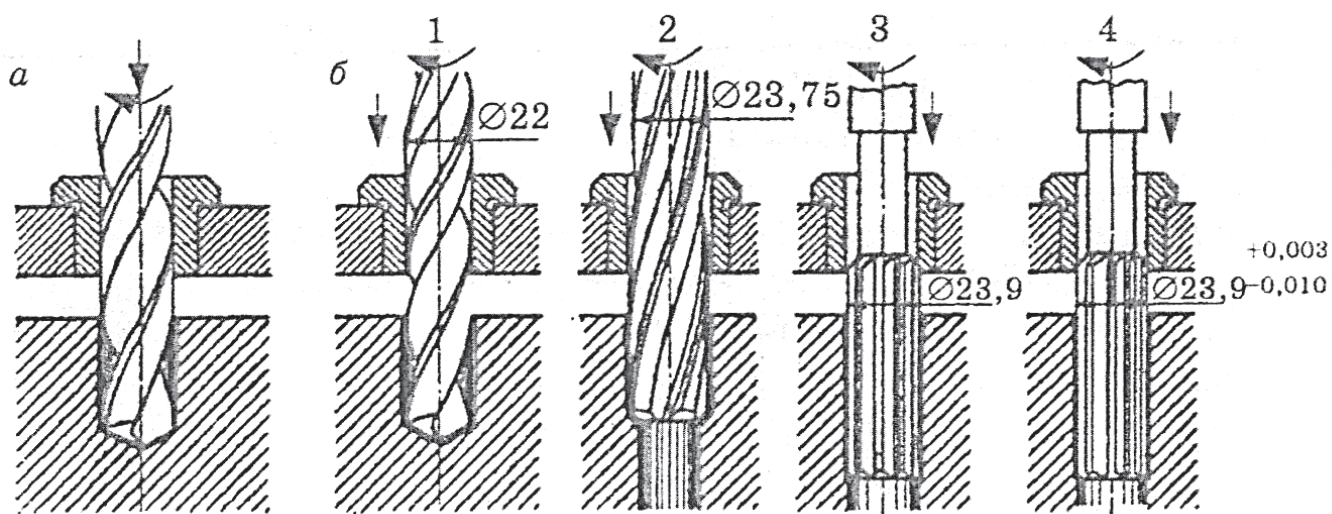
Обработка отверстий в сплошном материале: а – сверление отверстия 11...12-го квалитетов точности; б – обработка отверстий до 7-го квалитета точности; 1 – сверление; 2 – зенкерование; 3 – черновое развертывание; 4 – чистовое развертывание
